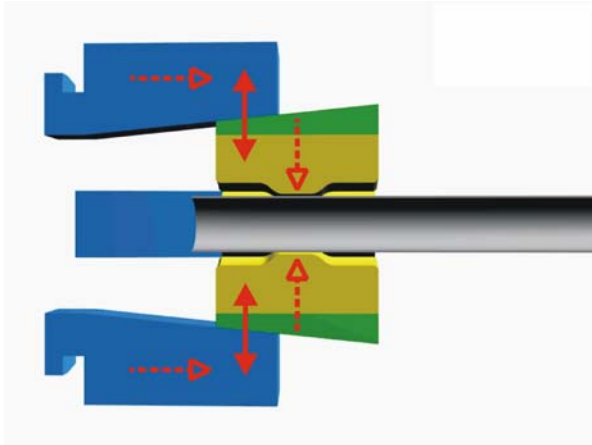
Einstechkneten – geöffnetes Werkzeug
